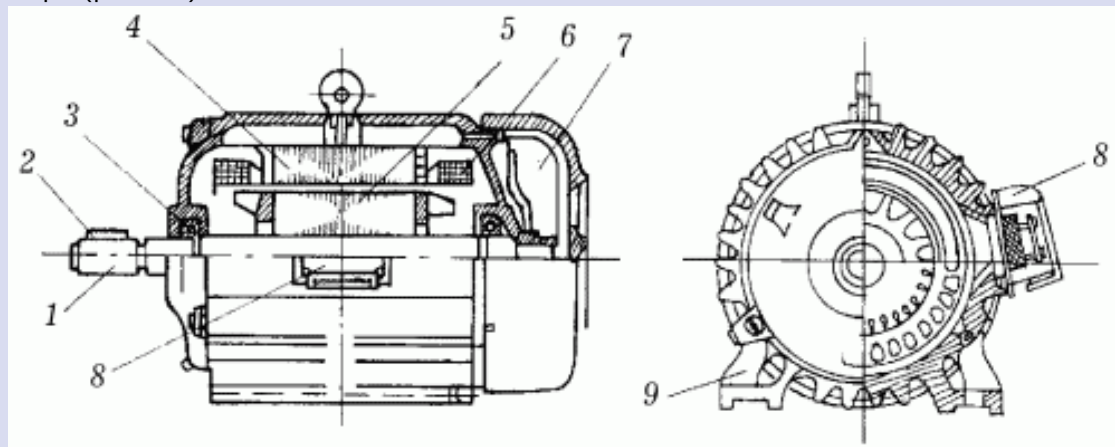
Устройство трехфазного двигателя серии 4А: 1 – вал; 2 – фиксирующая шпонка; 3 – подшипник; 4 – статор; 5 – обмотка статора; 6 – ротор; 7 – вентилятор; 8 – коробка выводов; 9 – лапа.
